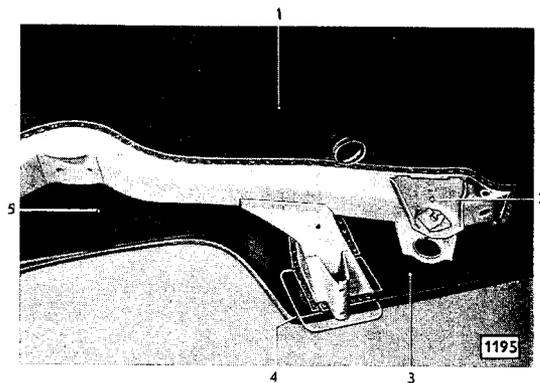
Hinterlängsträger mit Längsträgerzwischenstück an Bodenblech und Bodenblechseitenteil punktschweißt
